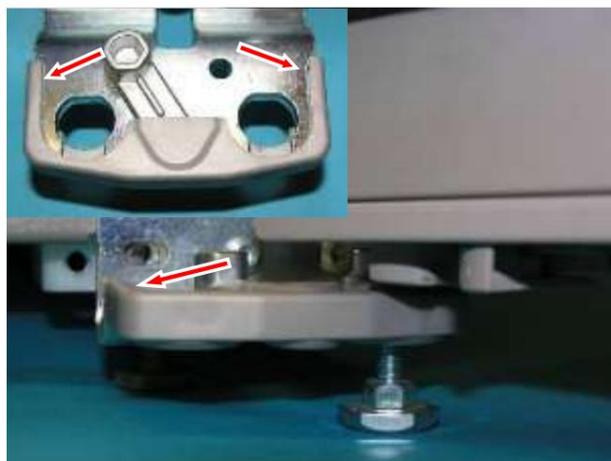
/ 1 Couvercle de charnière tournante
